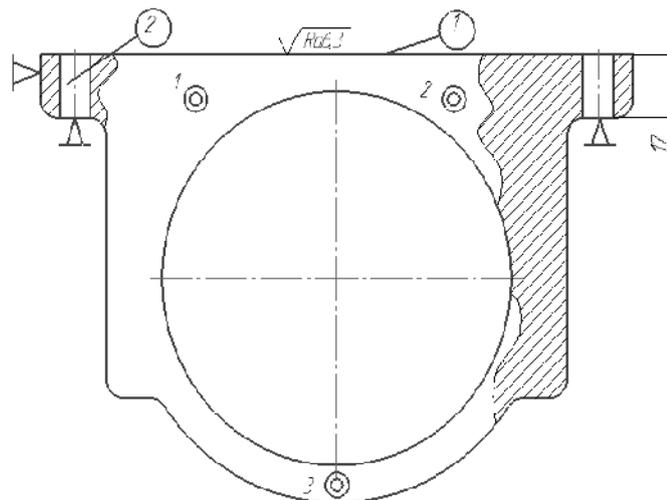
Схема установки заготовки на тактовому столі
